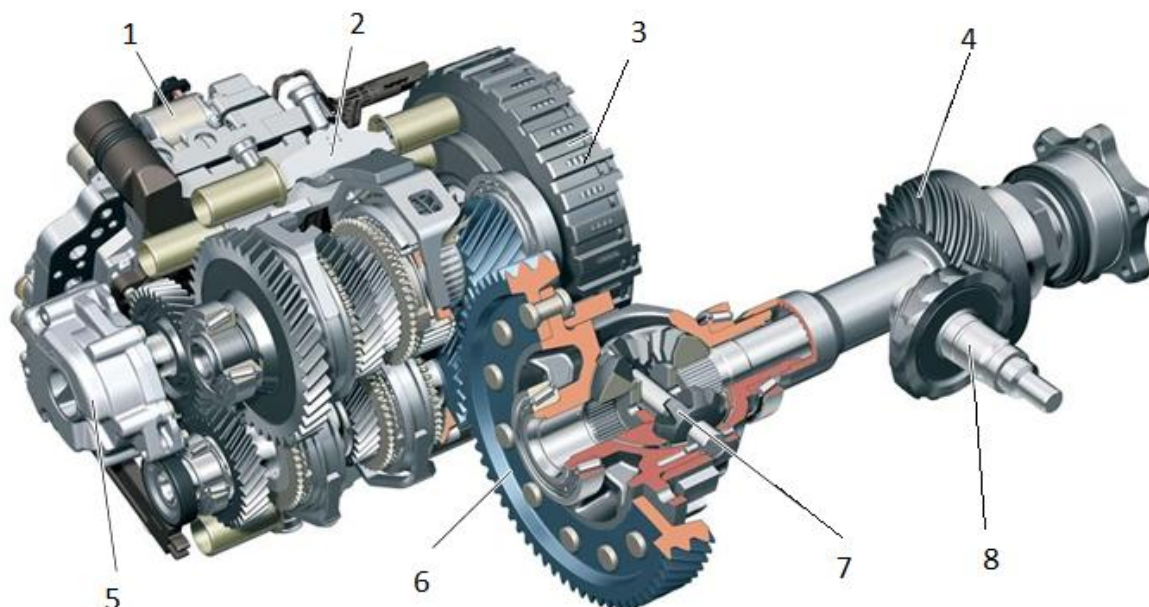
Вид с главной передачей и угловым редуктором (угловой редуктор только для полноприводных автомобилей):
